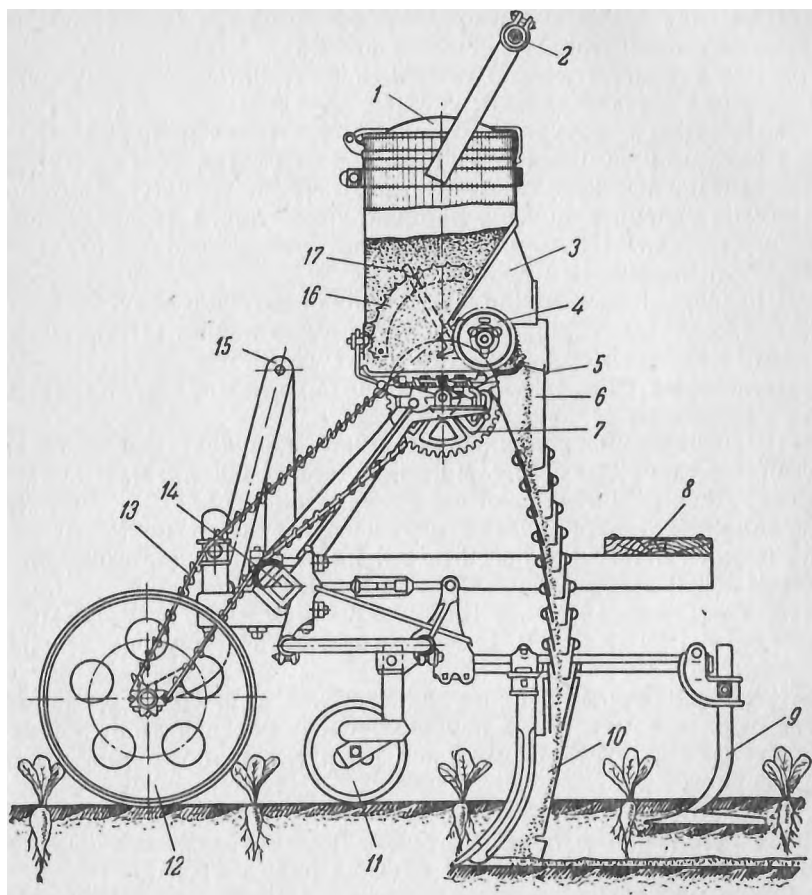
Схема культиватора-растениепитателя КРН-2,8 с подкормочным приспособлением:
